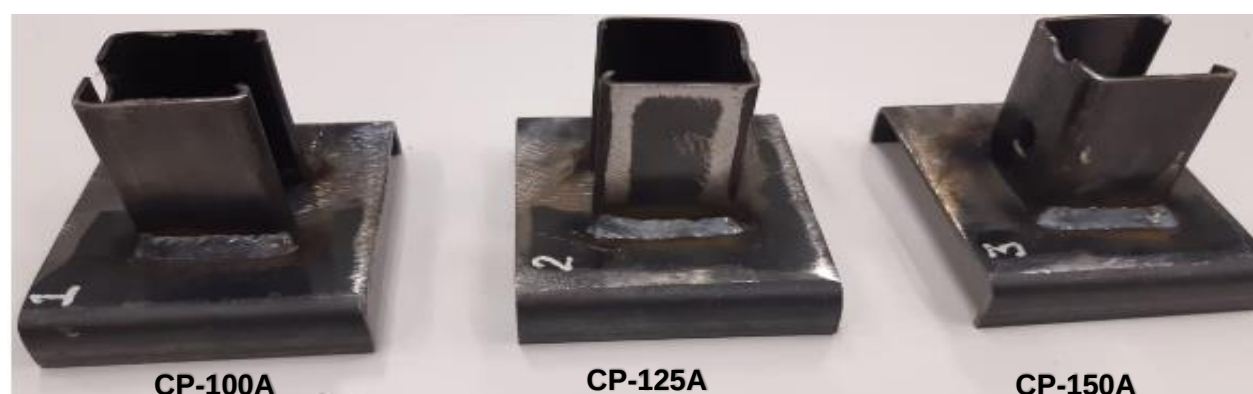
Amostras soldadas com arame Ø 0,8 mm
